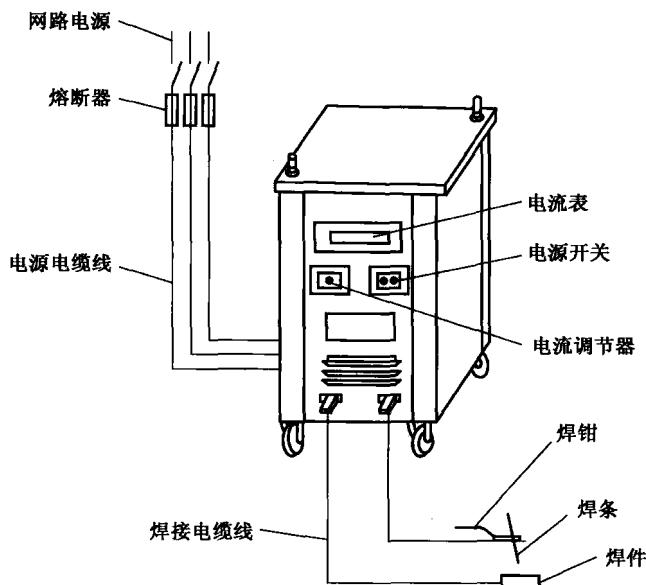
ZXG-300 型硅弧焊整流器的外形及外部接线
